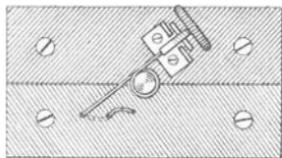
Bremsvorrichtung bei Lager mit Rillenführung.
